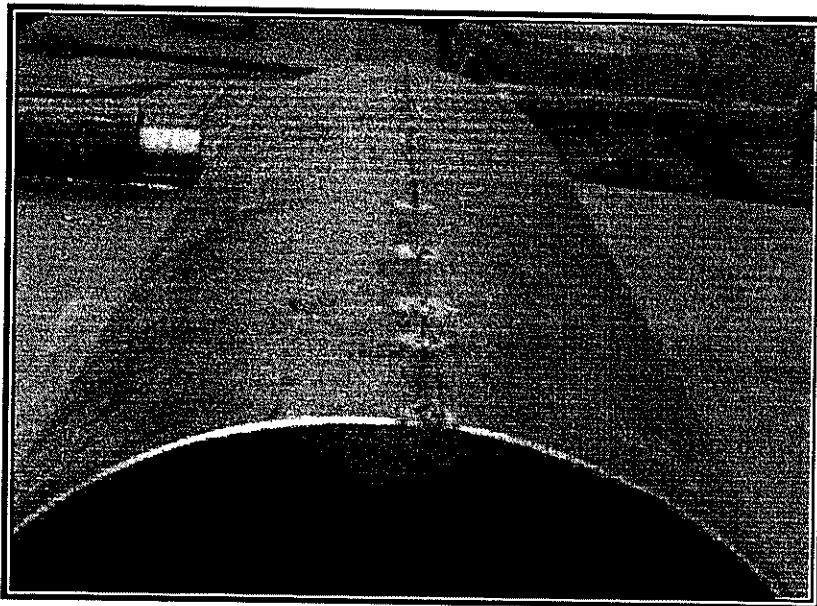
CHAPA DE ACERO CILINDRADA Y SOLDADA CON PUNTOS
